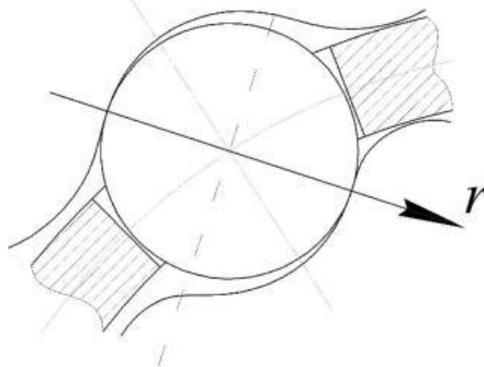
Схема контакта тела качения с циклоидальными профилями зубчатых колес
